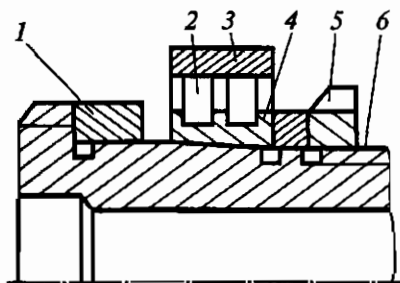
Схема регулирования предварительного натяга роликоподшипника серии 3182100:
